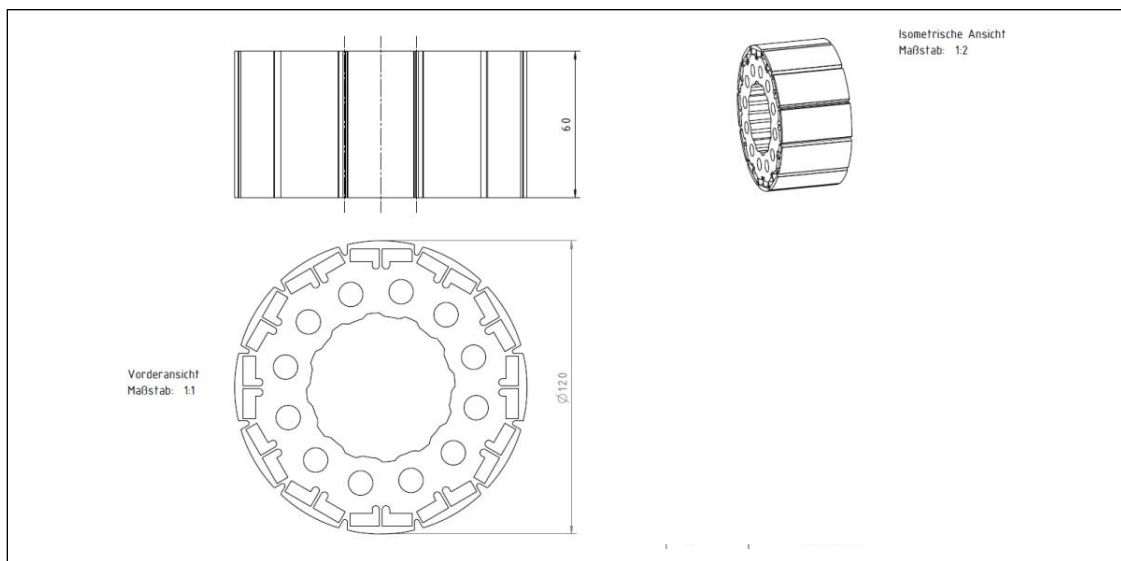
Rotorblechschnitt und -teilkpaket des Motors M1
